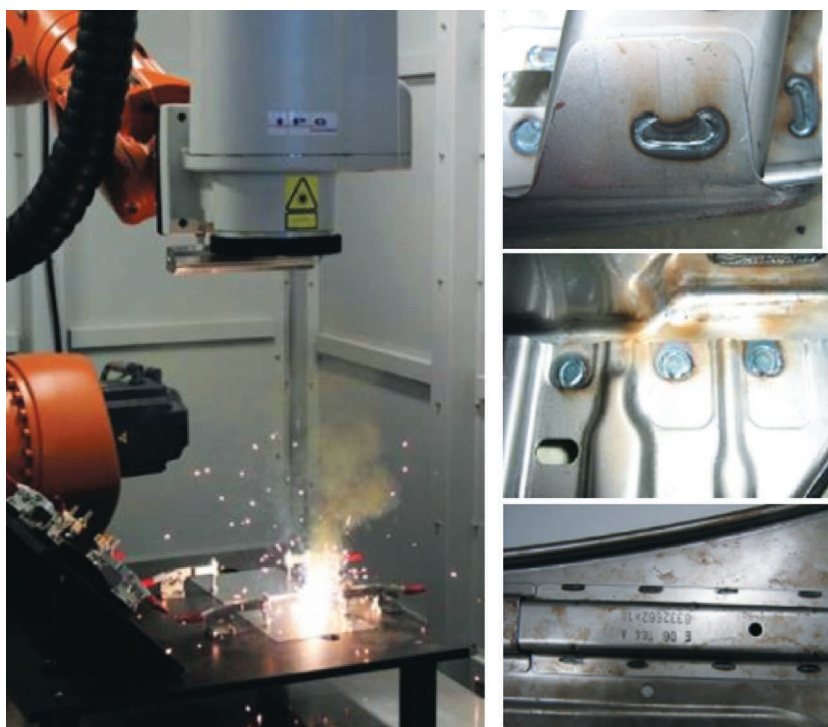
Устройство удаленной лазерной сварки [5]
